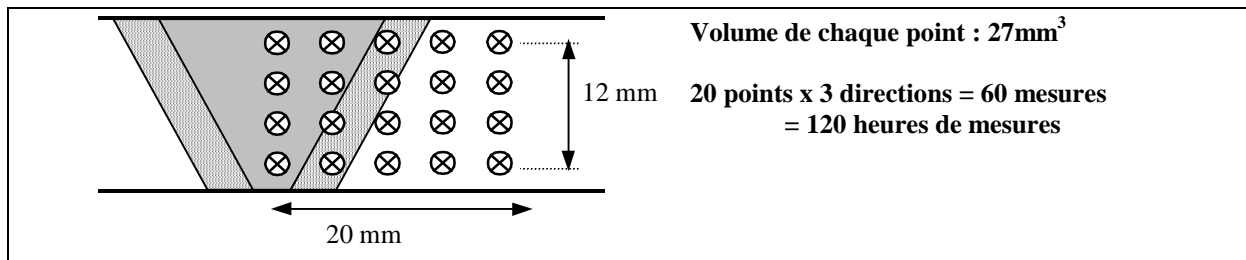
Grille de points de mesure des contraintes résiduelles dans la section du joint soudé.
